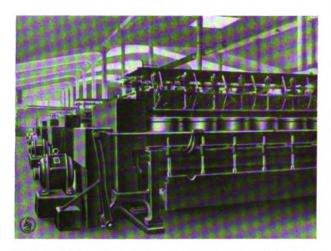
Schlauchkops-Spinnmaschinen, angetrieben durch Kurzschlußläufermotoren.
